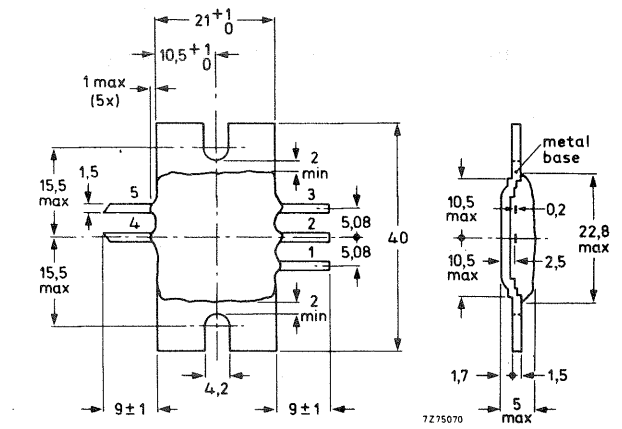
(a): - Dimensioni d'ingombro in mm dei moduli OM 320, OM 321, OM 335;
